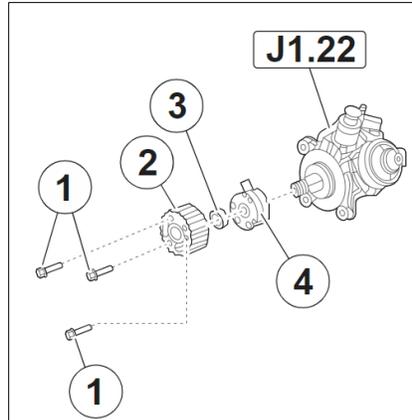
Piezas desmontaje bomba de alta presión CP4
